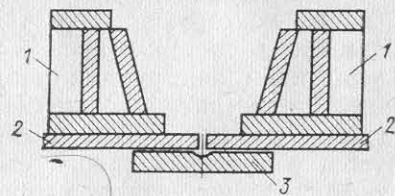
Схема установки листов при сборке под сварку.
